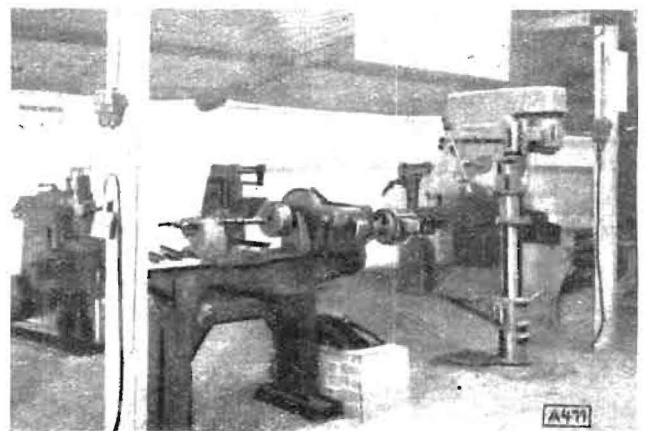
Innenansicht einer modernen MAS-Reparaturwerkstatt
